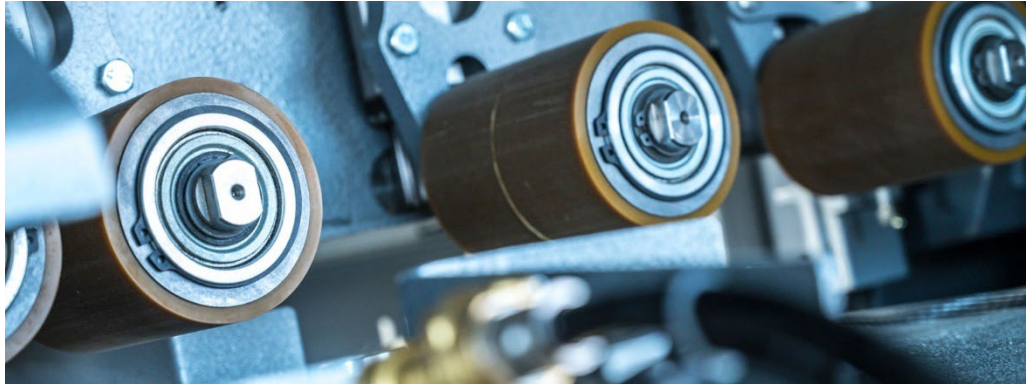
Detail Kappanlage CNC (Quelle: Paul Maschinen Fabrik GmbH & Co. KG)
